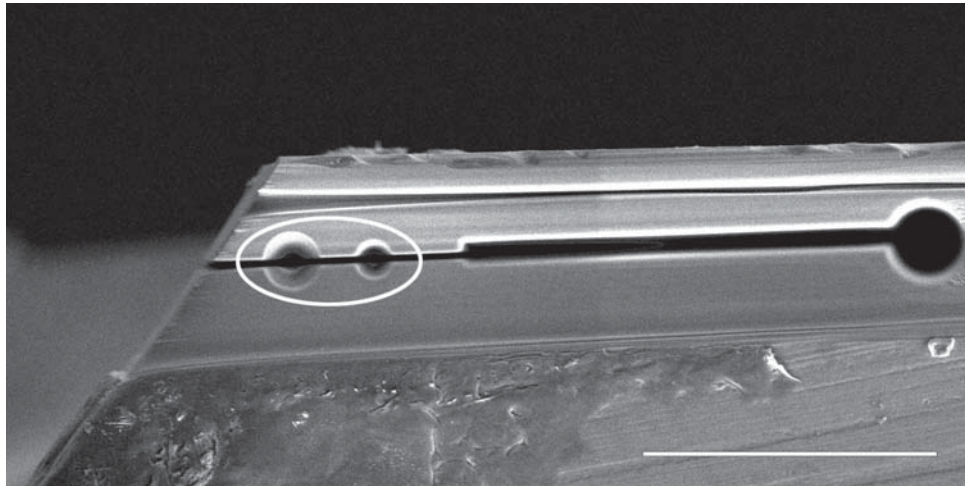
Seitensicht eines rückfedernden Umformwerkzeugs mit zwei Rundsätteln verschiedenen Durchmessers (siehe ovale, weiße Markierung) für die schrittweise Querschnittsreduzierung von stabförmigen Halbzeugen. (Maßstab: 30 μm)
